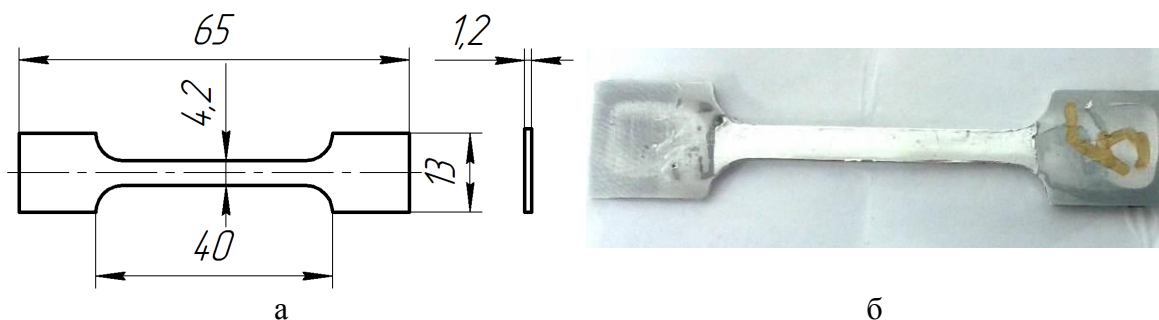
Чертеж образца технически чистого алюминия А1 для испытаний (а) и фотография образца (б)
